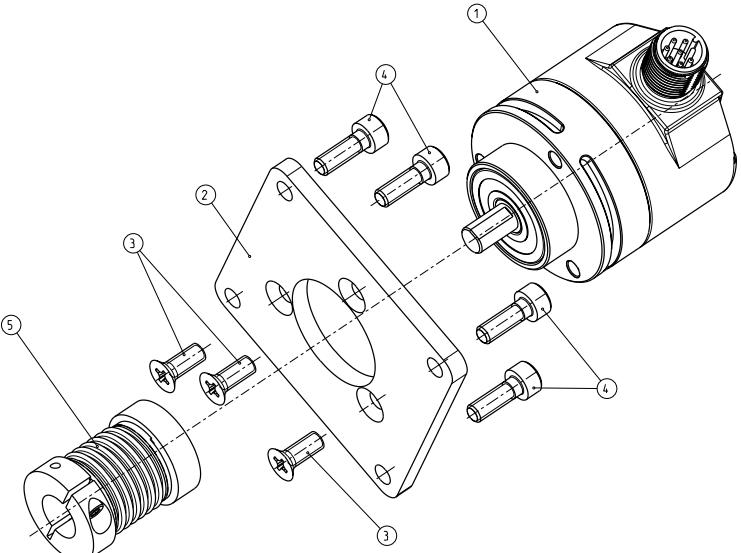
Disegno di assemblaggio SKS36S/SKM36S stand alone con piastra di montaggio
